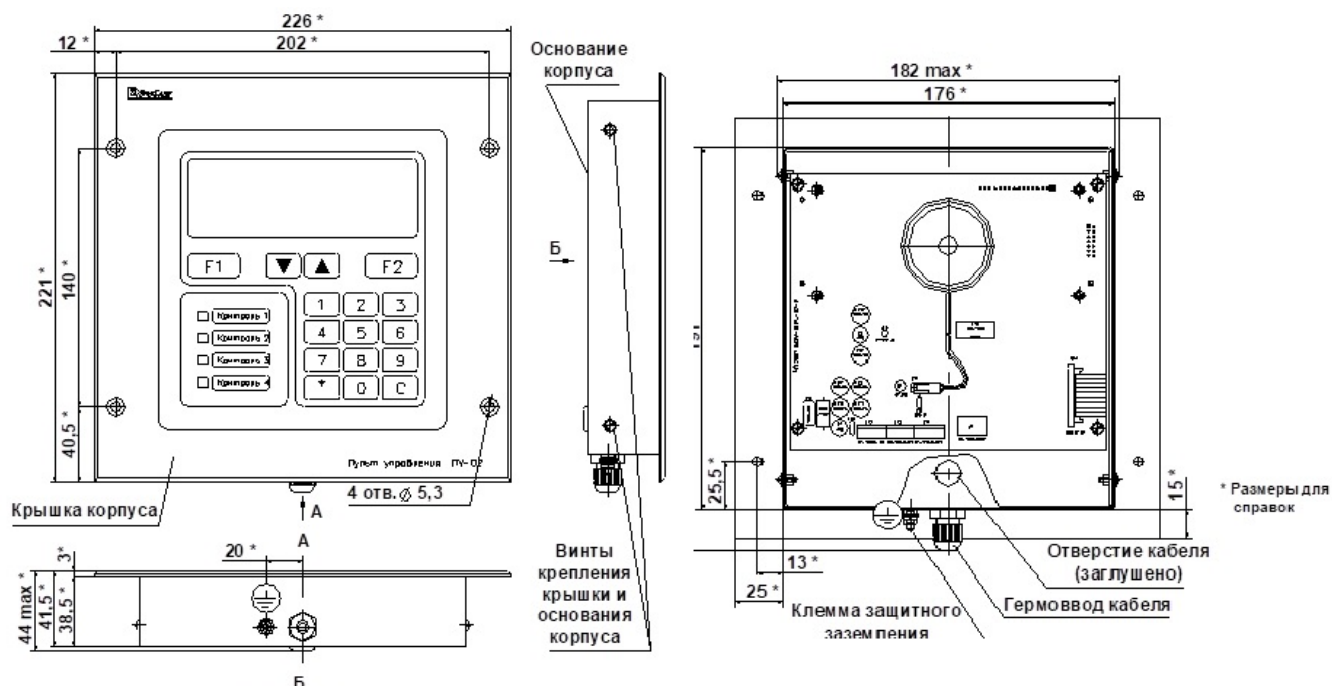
Габаритные и присоединительные размеры (врезное исполнение Тип 1)
